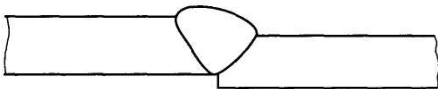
Сварное соединение со смещением кромок и непроваром по кромке свариваемого элемента
